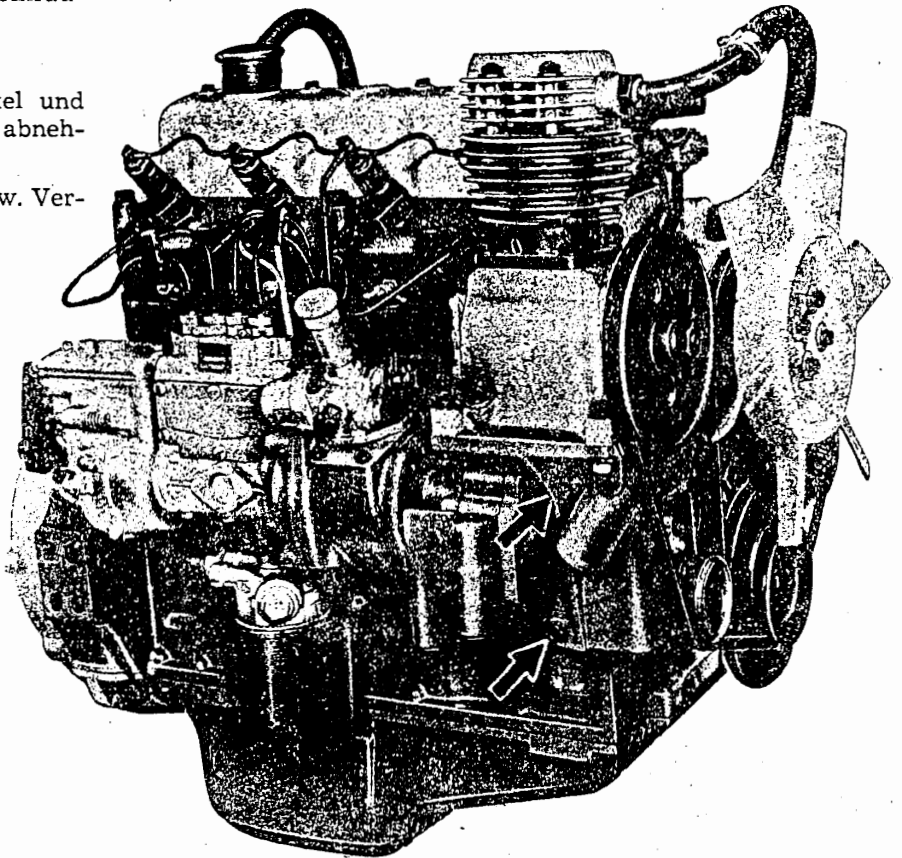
Befestigungsschrauben für Konsol aus Kurbelgehäuse mit Drehmomentschlüssel mit 35 Nm (3,5 kpm) anziehen
